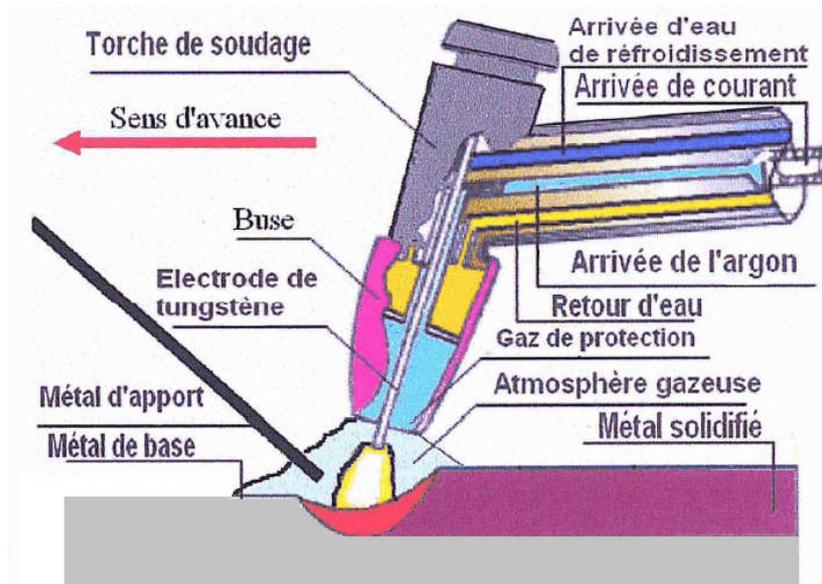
Soudage sous gaz inerte [3-4].
